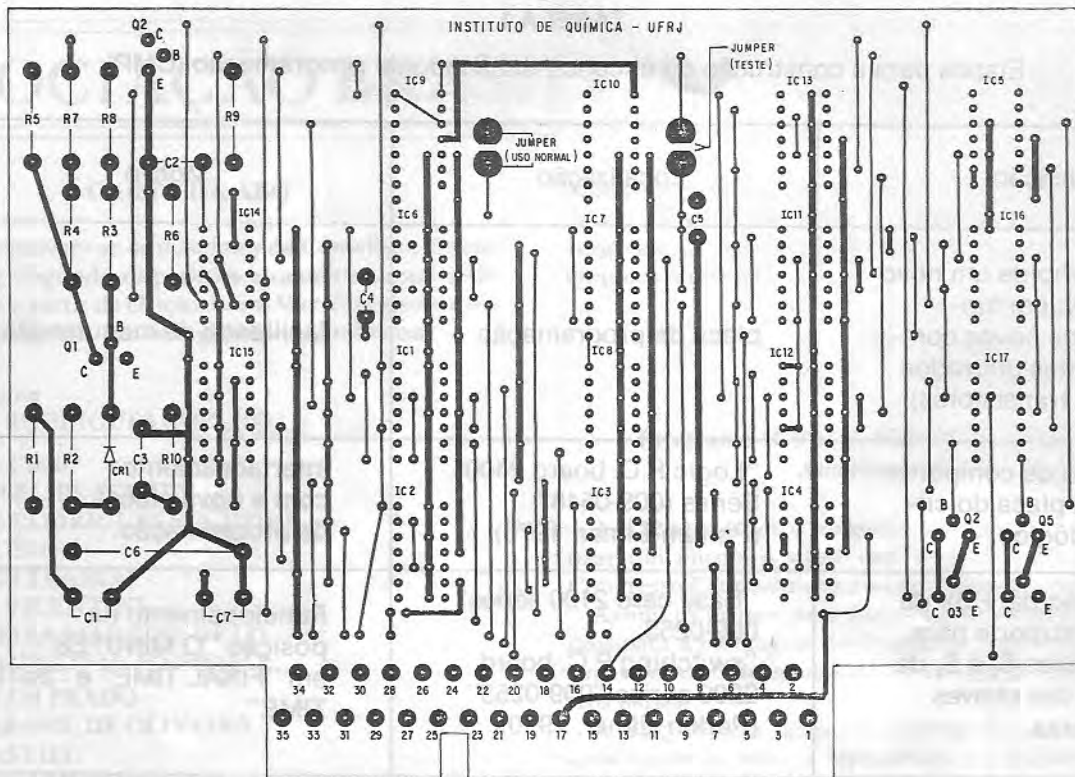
A Placa de circuito impresso — face superior (lado dos componentes).
